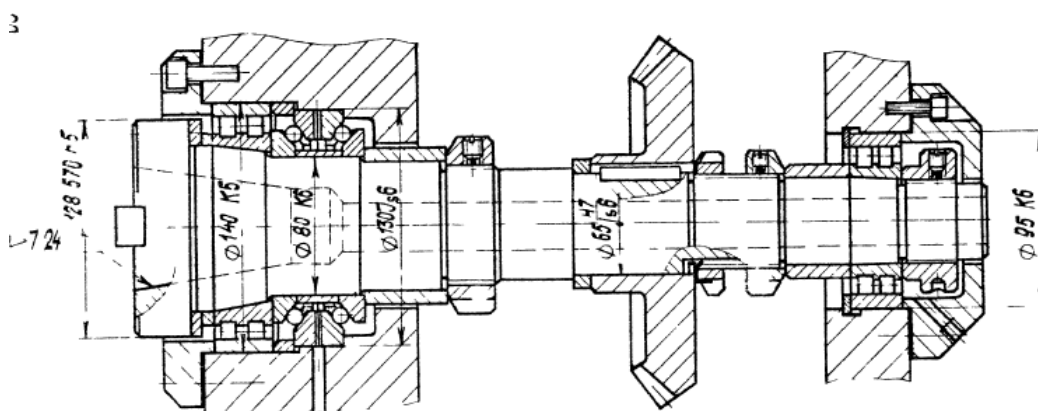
Пример чертежа конструкций шпиндельного узла
